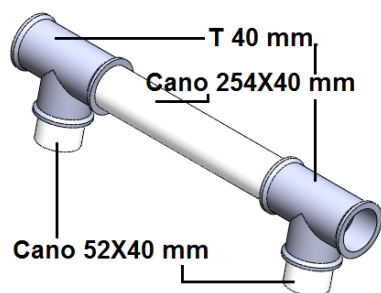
Montagem dos módulos – Módulo 2 – Passo 1
